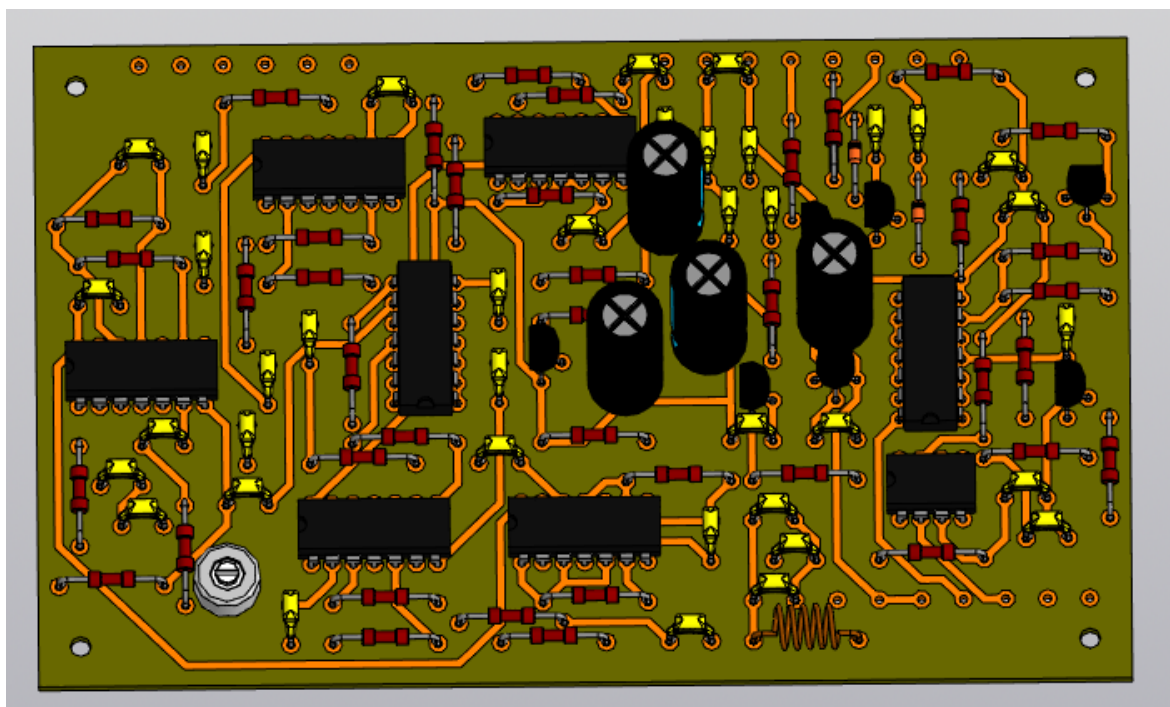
3D зображення вузла друкованого металодетектора основний вигляд зверху
